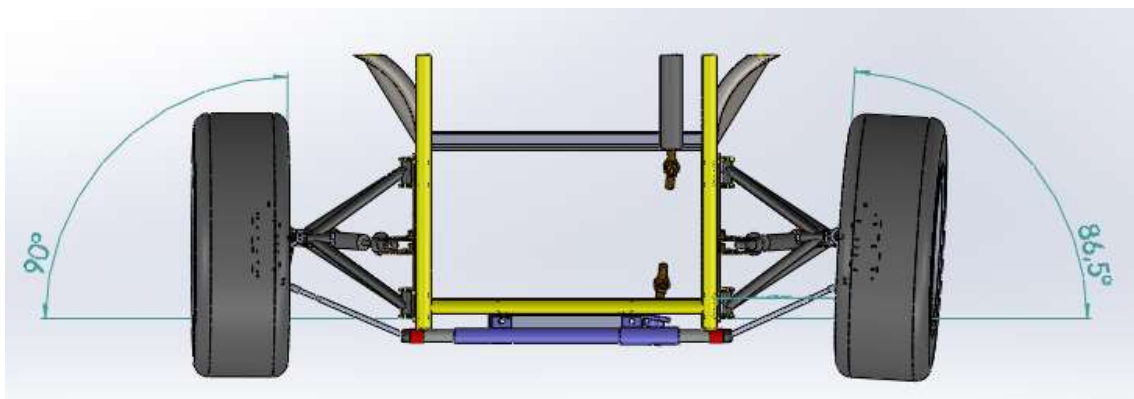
Efeito Bump Steering caixa direção abaixo (vista superior)
